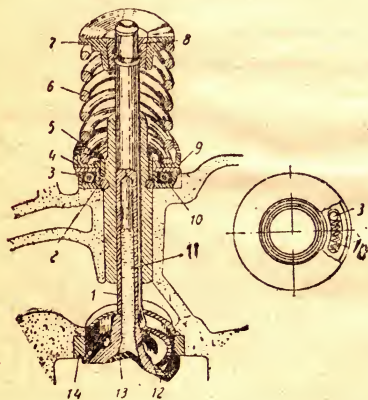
Выпускной клапан двигателя ЗИЛ-130 с механизмом поворачивания:
